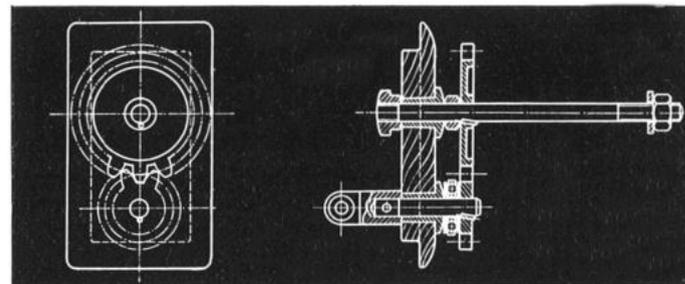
Supporto ad ingranaggi, demoltiplicatore di giri.
